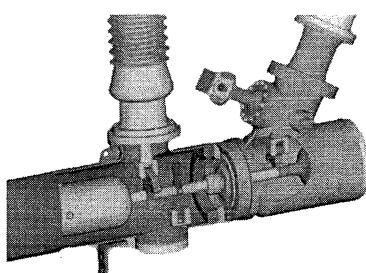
Двойной комбинированный разъединитель-заземлитель для применения с двойной системой шин (на рисунке оба разъединителя показаны подключенными к различным сборным шинам)
